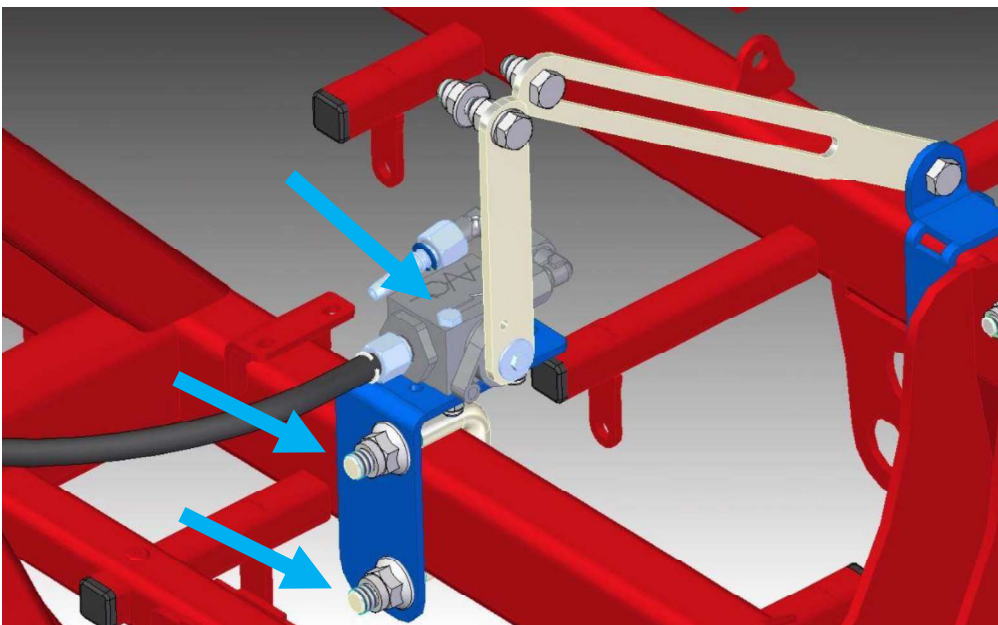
Montage des Befestigungsbleches und Hubbegrenzers am Mittelrahmen
